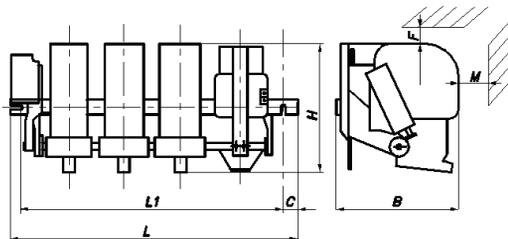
Общий вид и габаритные размеры КТ-6600.
